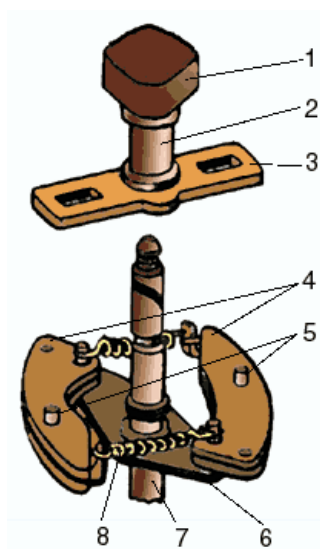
Конструкция центробежного регулятора угла опережения зажигания: 1 - кулачок прерывателя; 2 - втулка кулачков; 3 - подвижная пластина; 4 - грузики; 5 - шипы грузиков; 6 - опорная пластина; 7 - приводной вал; 8 – стяжные пружины
